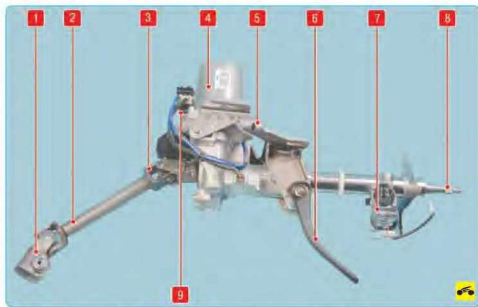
Рулевая колонка: 1 – нижний карданный шарнир промежуточного вала; 2 – промежуточный вал; 3 – верхний карданный шарнир промежуточного вала; 4 – моторредуктор электроусилителя рулевого управления; 5 – кронштейн крепления рулевой колонки; 6 – рычаг регулировки положения рулевой колонки; 7 – выключатель (замок) зажигания; 8 – рулевой вал; 9 – электронный блок управления системой электроусилителя рулевого управления
